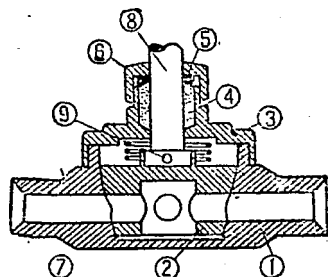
Кран с пробковым конусом: 1—корпус крана, 2—пробковый конус, 3—крышка корпуса, 4—сальник, 5—прокладки, 6—гайка, 7—канал для горючего, 8—тяга управления краном, 9—пружина конуса.
